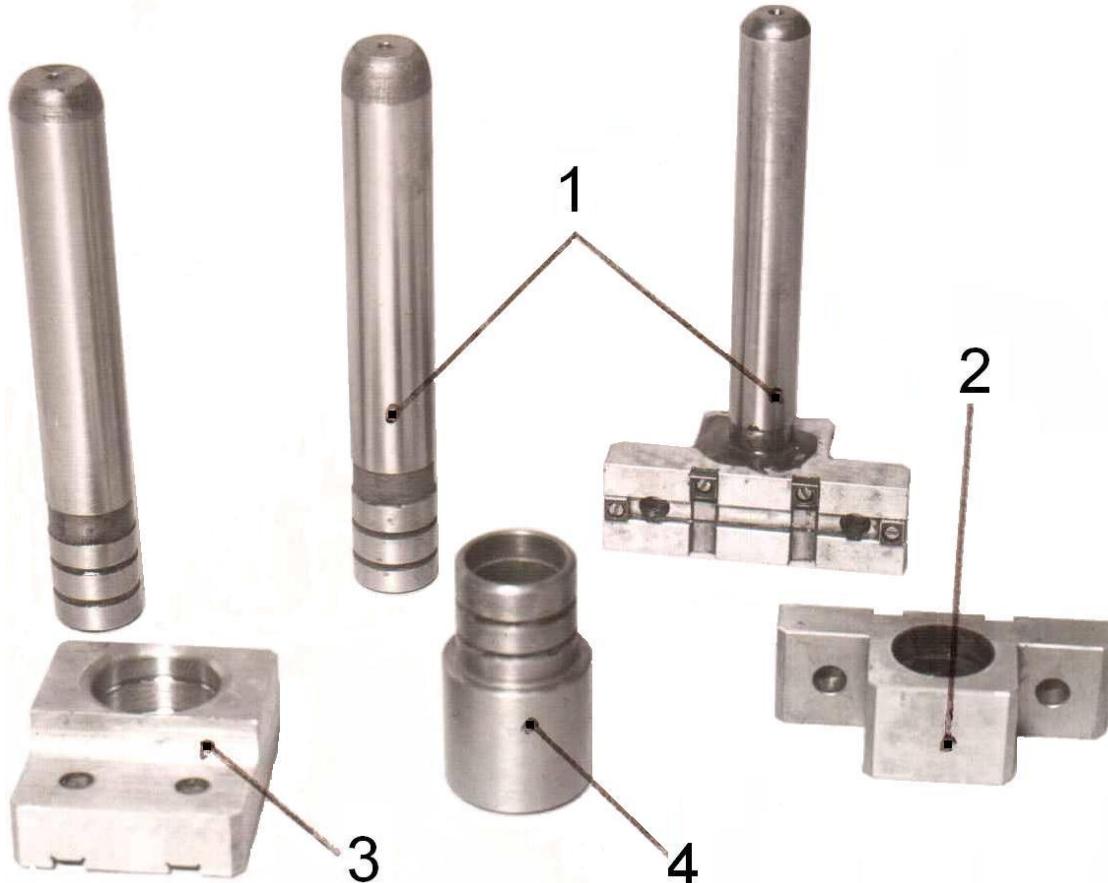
Направляющие элементы: а – УСПШ-16; б – УСПШ-8; 1 – направляющая колонка; 2 – нижняя обойма; 3 – верхняя обойма; 4 – направляющая втулка
